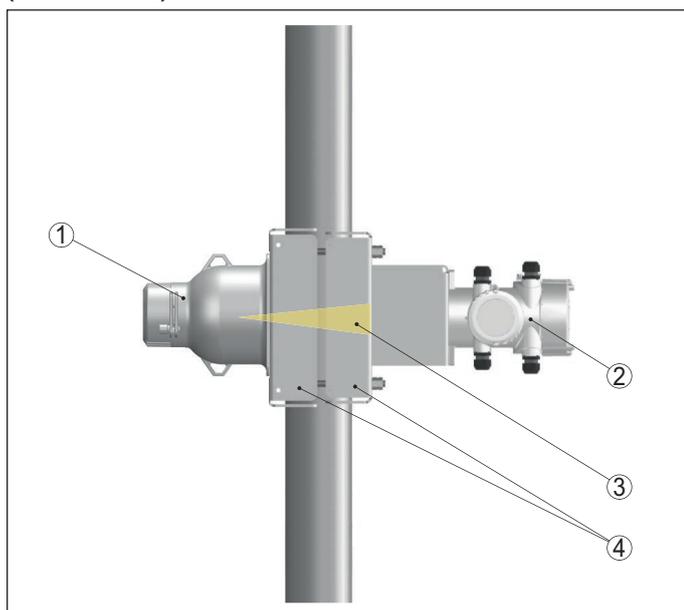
Dispositivo di fissaggio per montaggio su tubi da 50 ... 220 mm (1.97 ... 8.66 in)
